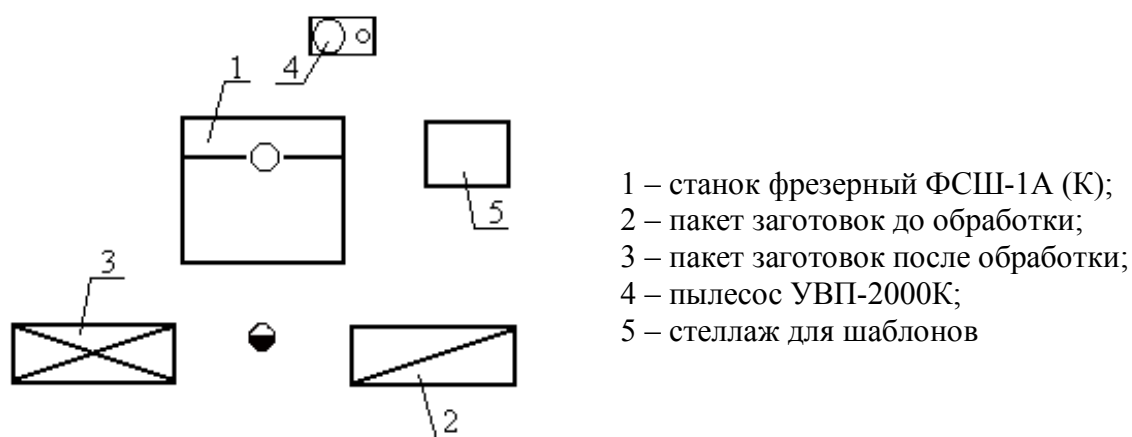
План рабочего места у фрезерного станка с шипорезной кареткой ФСШ-1А (К)
